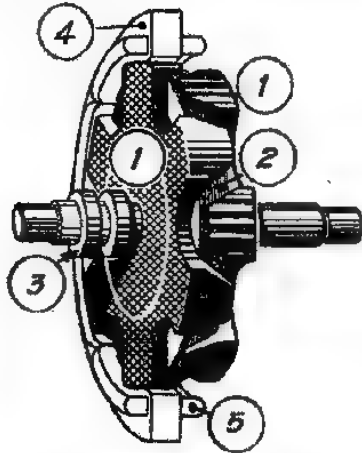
A. — Corte esquemático de un alternador para automotor.
